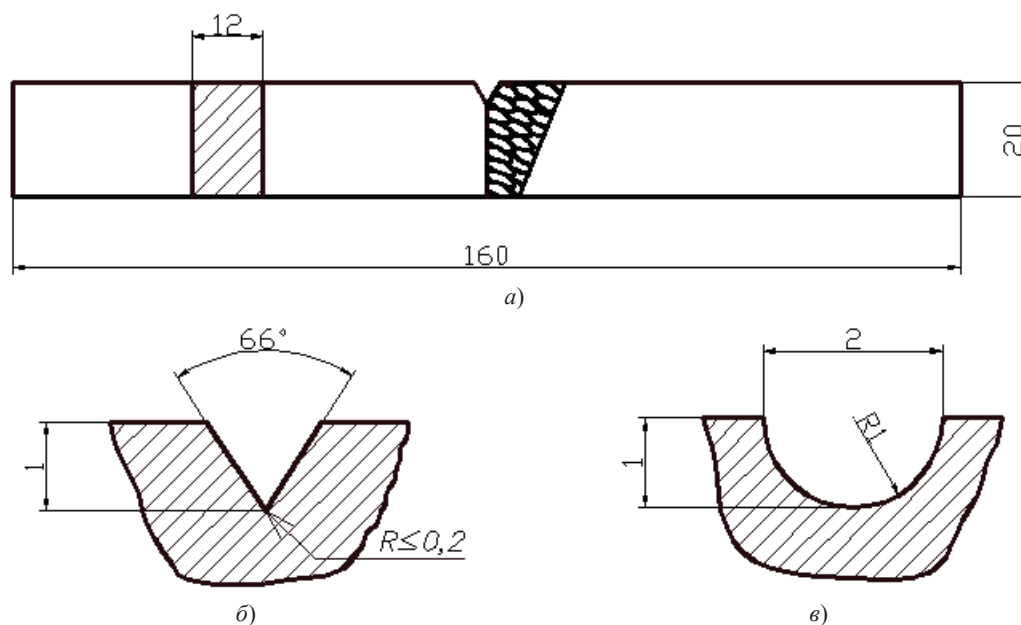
Плоский сварной образец (а) с краевым надрезом типа Шарпи (б) или Менаже (в)
